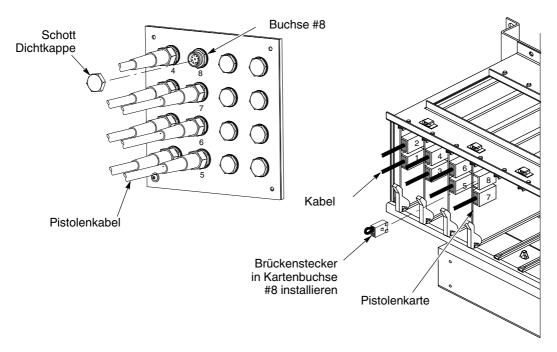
Dichtkappe und Brückenstecker installieren - Beispiel mit 7 Pistolen in einem System für 8 Pistolen
